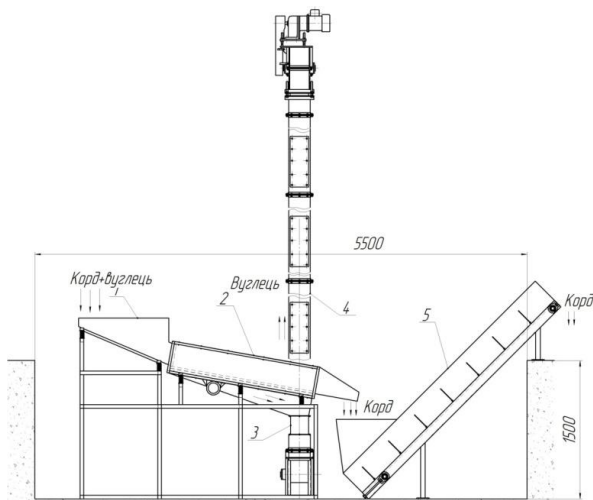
Технологічна схема для механічної очистки технічного вуглецю
